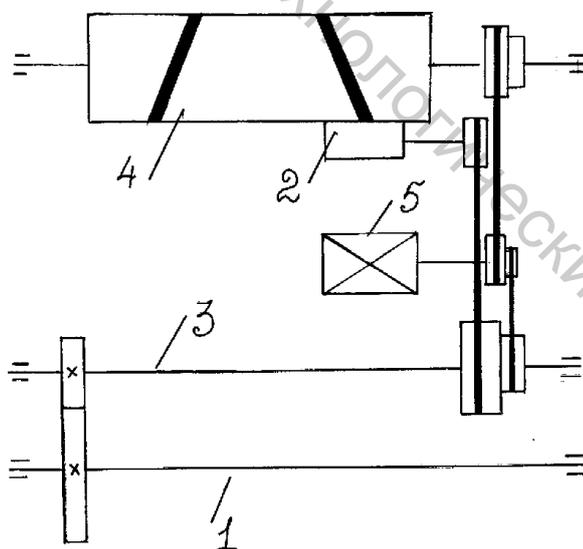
Кинематическая схема передачи движения рабочим органам мотальной головки
